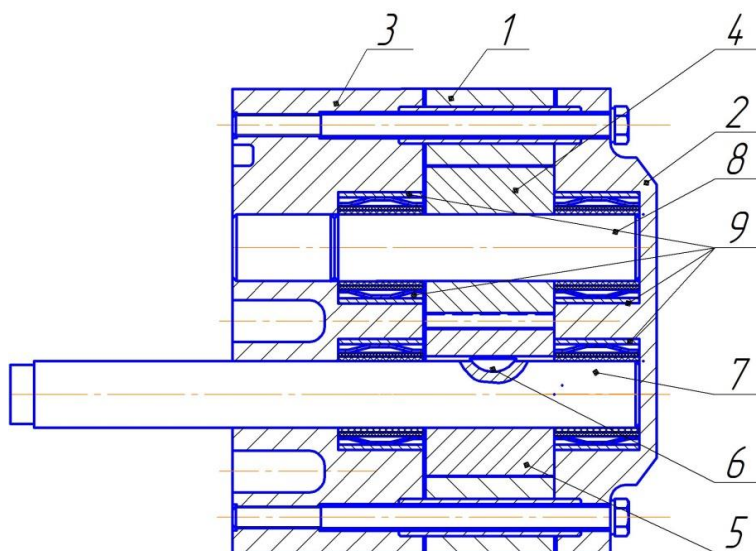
Загальний вид експериментального насоса підживлення з комбінованими втулками: 1 – корпус; 2 – верхня кришка; 3 – нижня кришка; 4 – ведена шестерня; 5 – ведуча шестерня; 6 – шпонка; 7 – вал ведучий; 8 – вісь веденої шестерні; 9 – комбіновані підшипникові втулки
